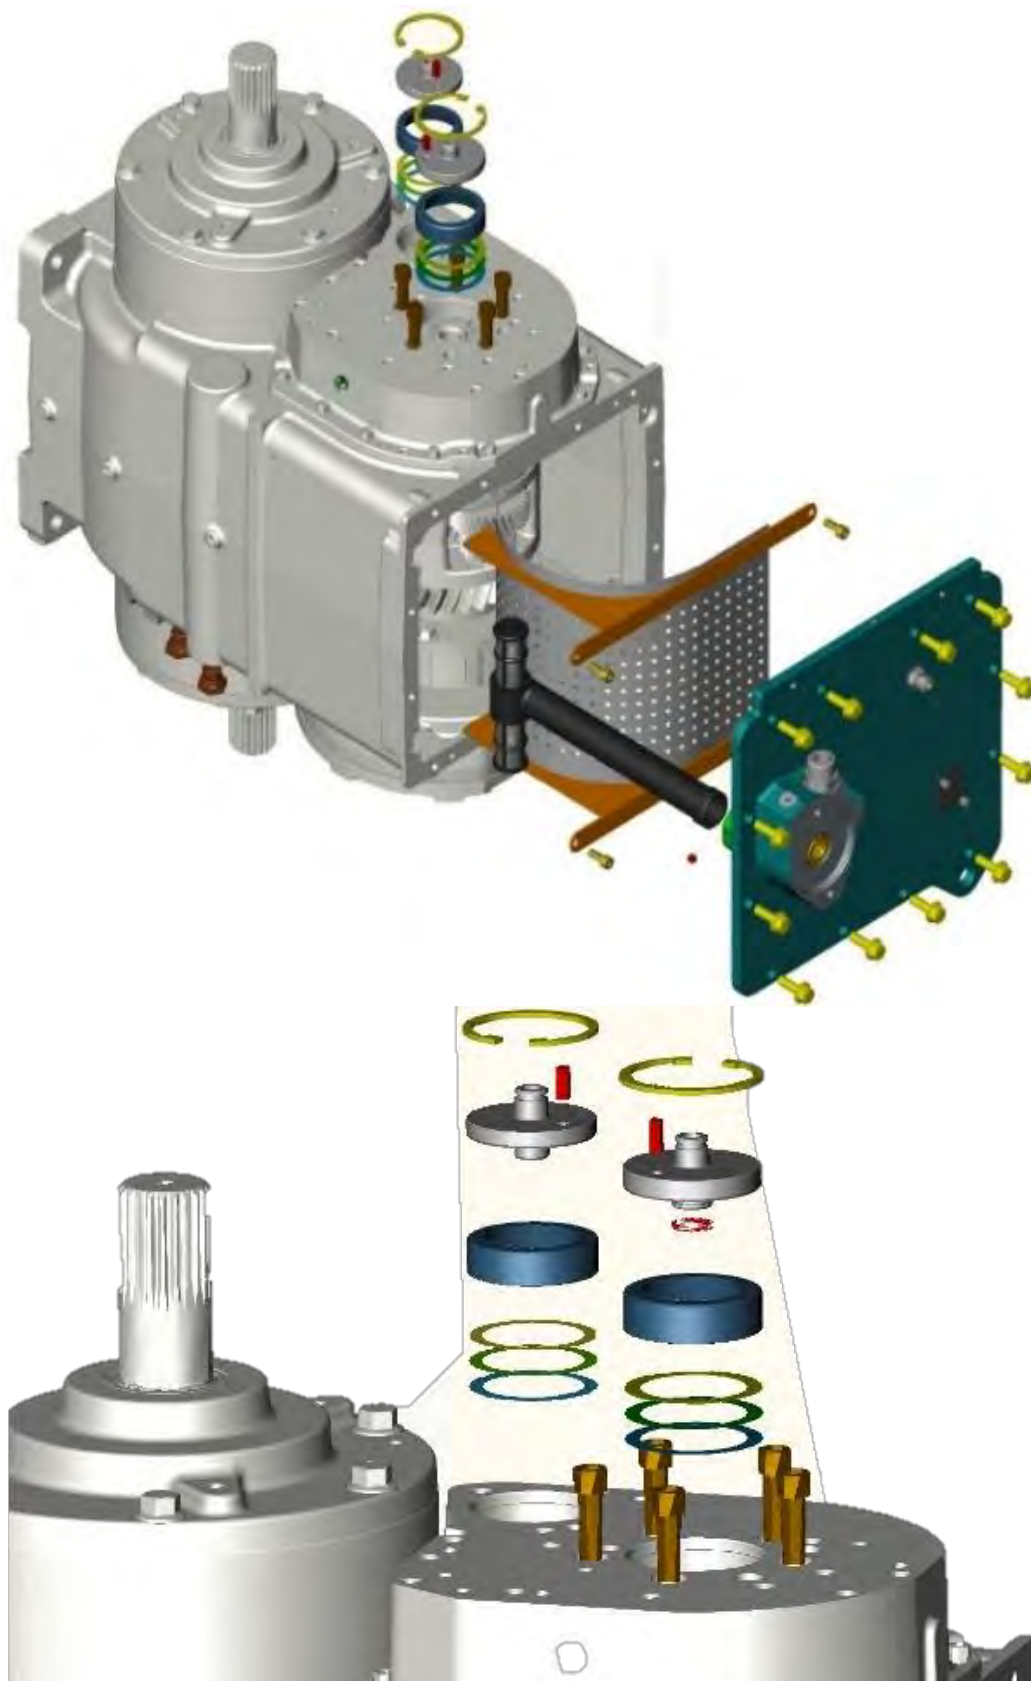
"Explosionado del proceso de montaje de la estación 4"
